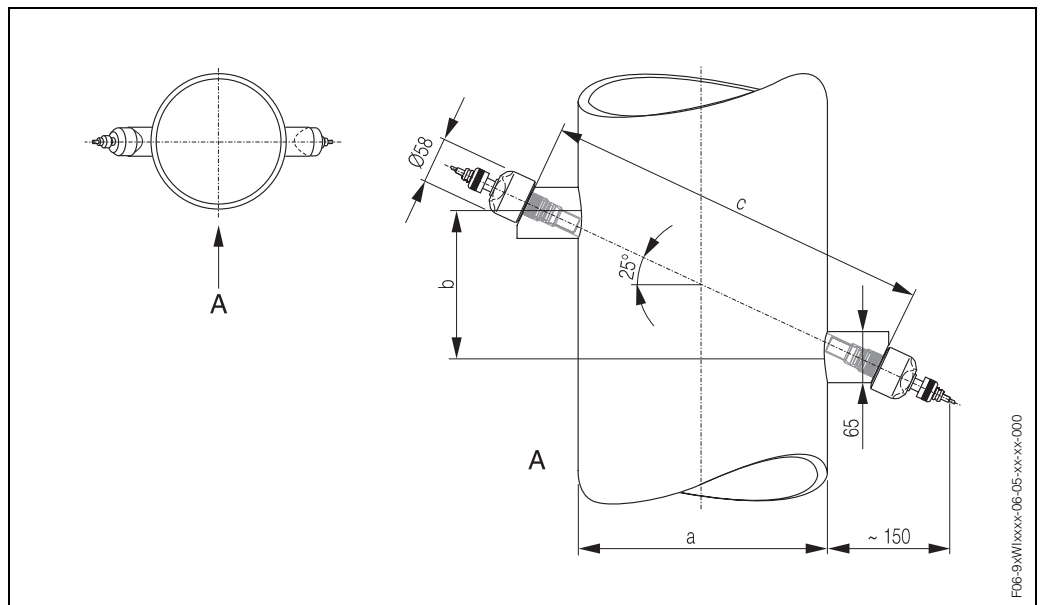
Dimensiones de los sensores W (versión de inserción)
